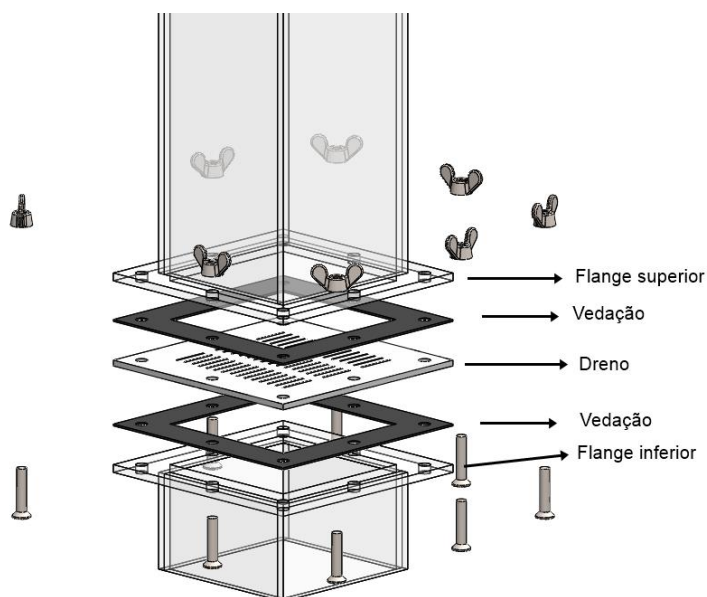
Detalhamento de fixação dos drenos ao dispositivo.
